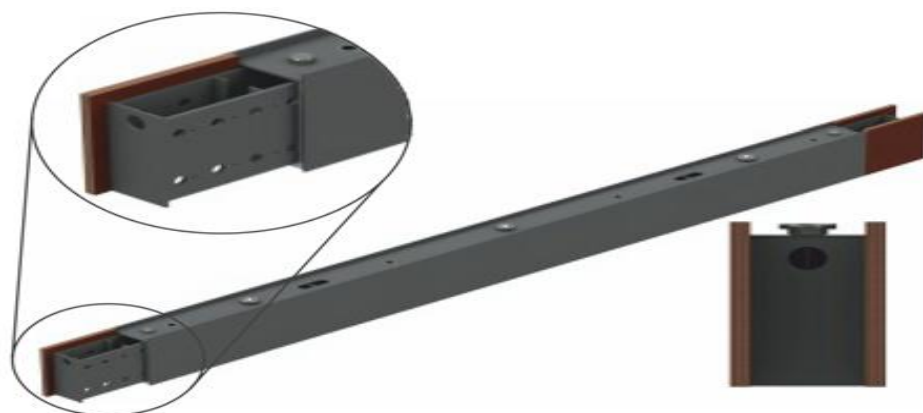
Подовження робочої поверхні сталевих бортів висувними планками
